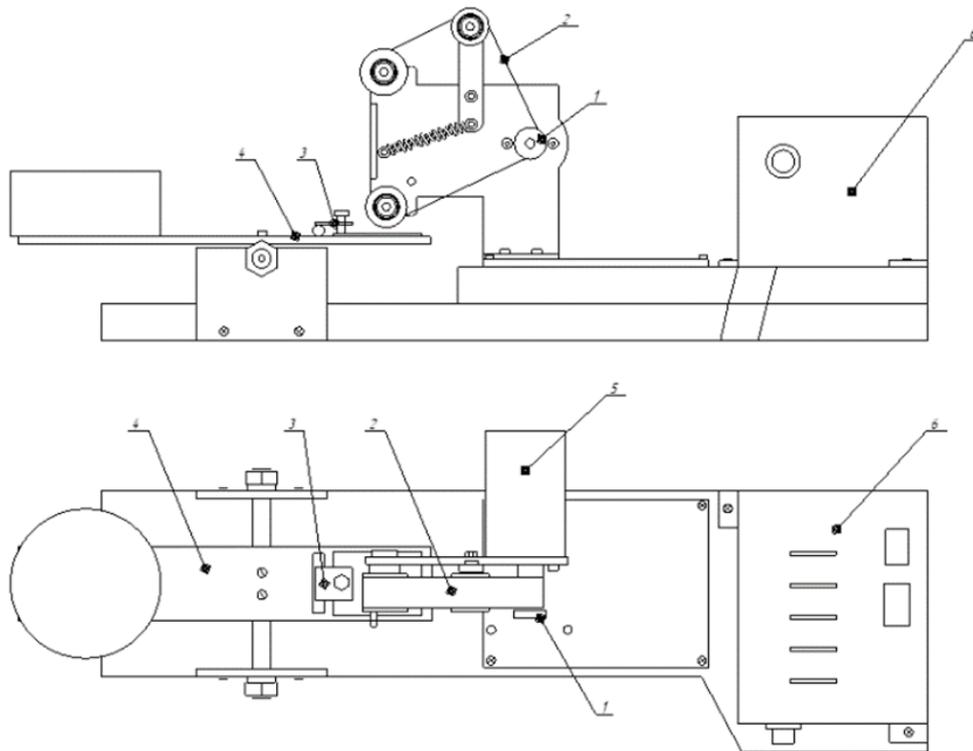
Схема установки ВИМ ЛТДП: 1- ротор с осью; 2 - абразивная лента; 3-держатель образца; 4 - рычаг; 5- электродвигатель, 6 – блок управления
